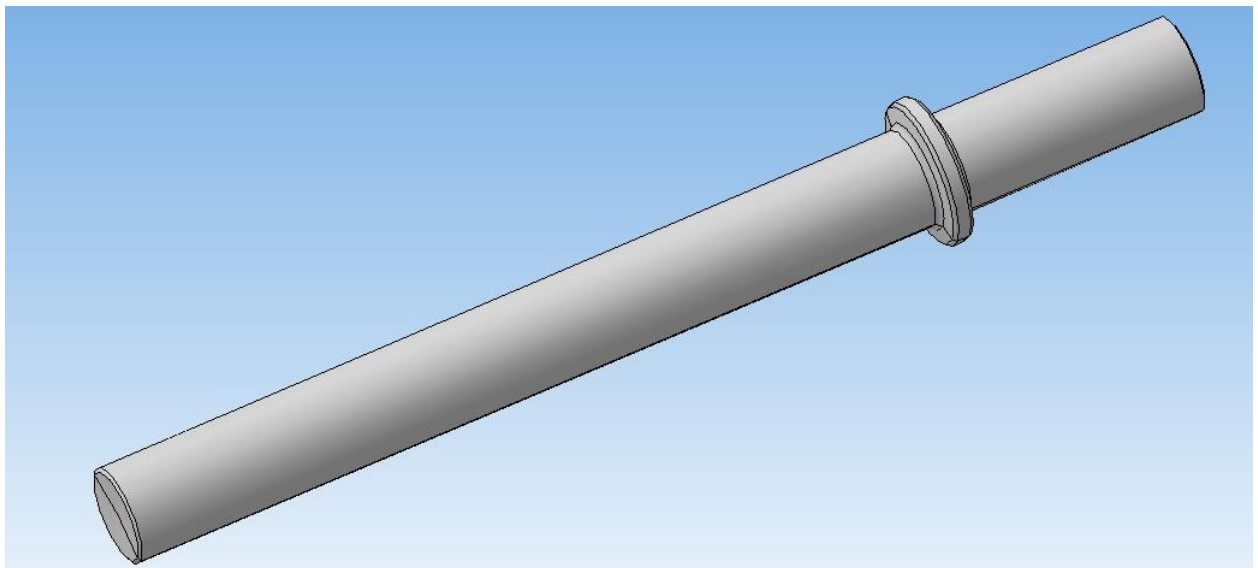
3D-модель штамповки заготовки для деталі «Гвинт БРД 210124»
